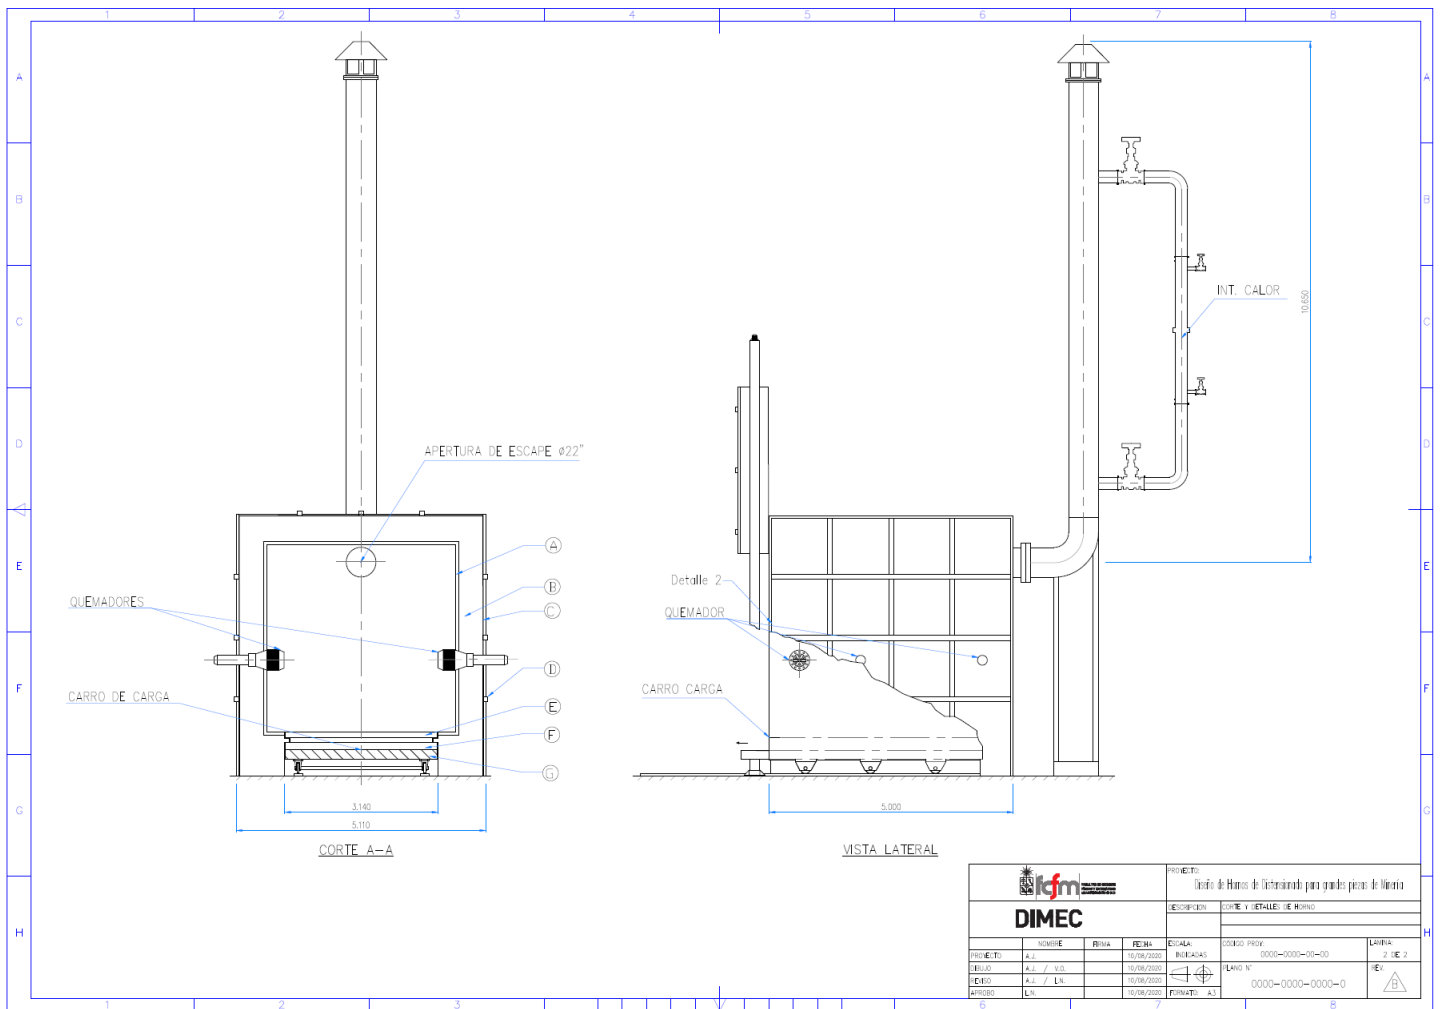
Corte A y detalle de perfil. Fuente: Elaboración propia.
